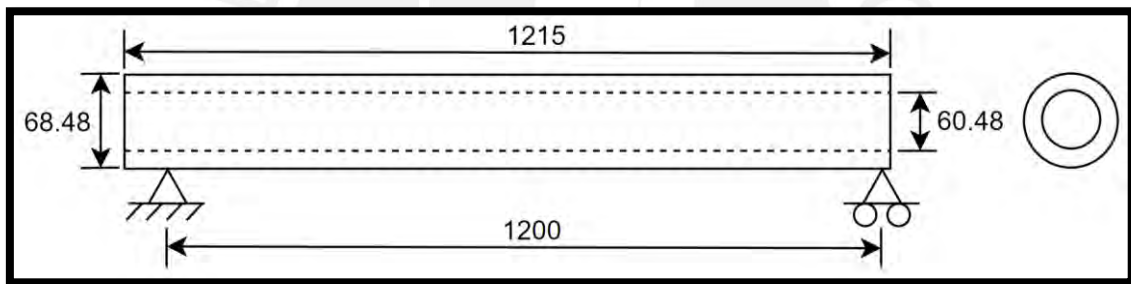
Apoyos y dimensiones de la cámara de fundición.
